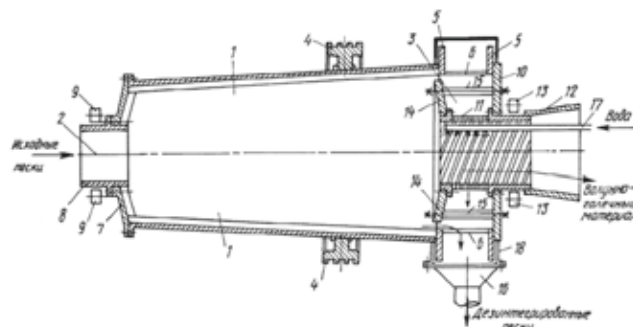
Схема промышленного дезинтегратора: 1 – барабан; 2 – загрузочное устройство; 3 – разгрузочное устройство; 4 – шкив передачи; 5 – фланцы; 6 – окна для разгрузки; 7 – загрузочная крышка; 8 – загрузочный патрубок; 9 – ролики; 10 – крышка; 11 – цапфа; 12 – диффузор; 13 – ролики; 14 – отбойная плита; 15 – крепление; 16 – приемный лоток; 17 – опрыскивательная труба; 18 – кожух /
